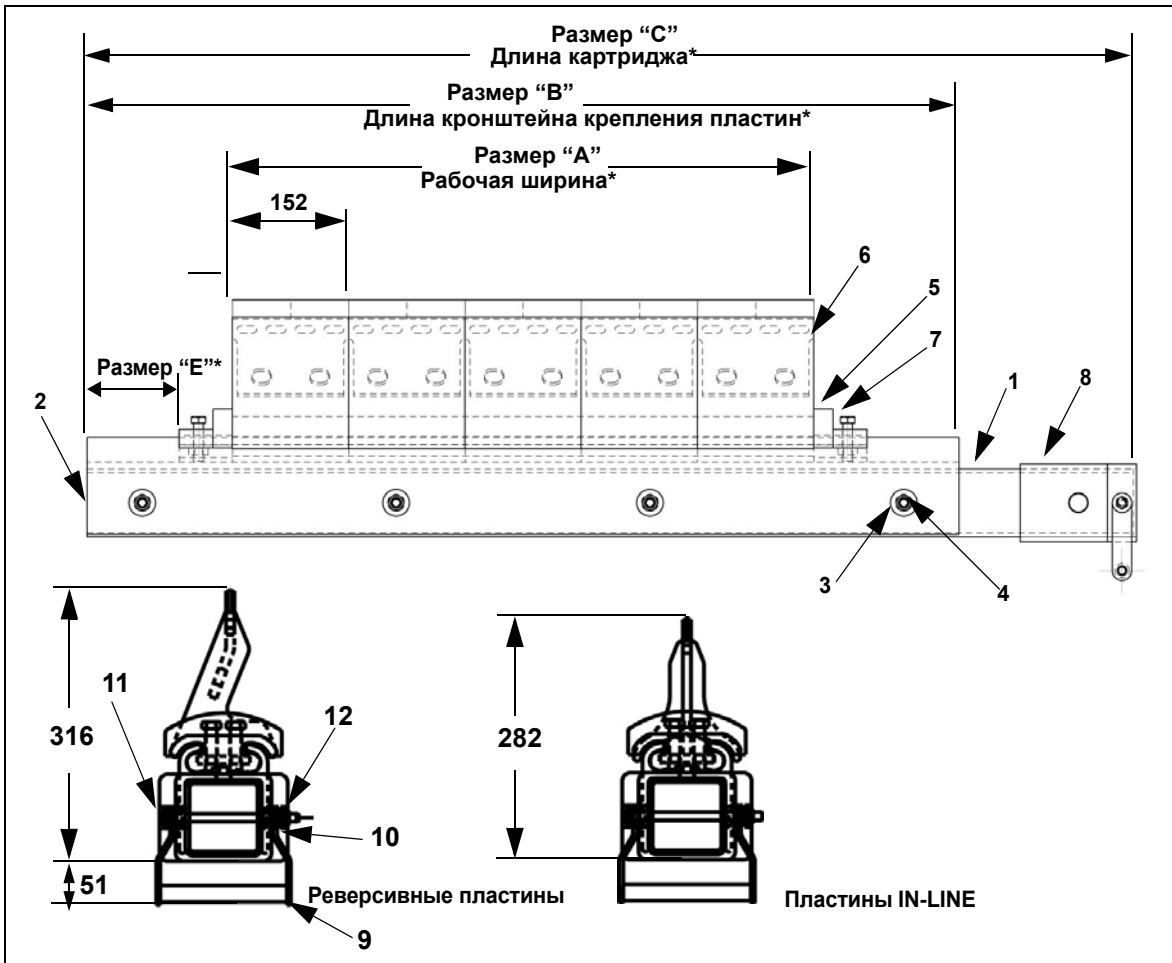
MARTIN® DT2H Основной скребок без натяжителя, артикул DT2HC-XXXXXXXXXX
